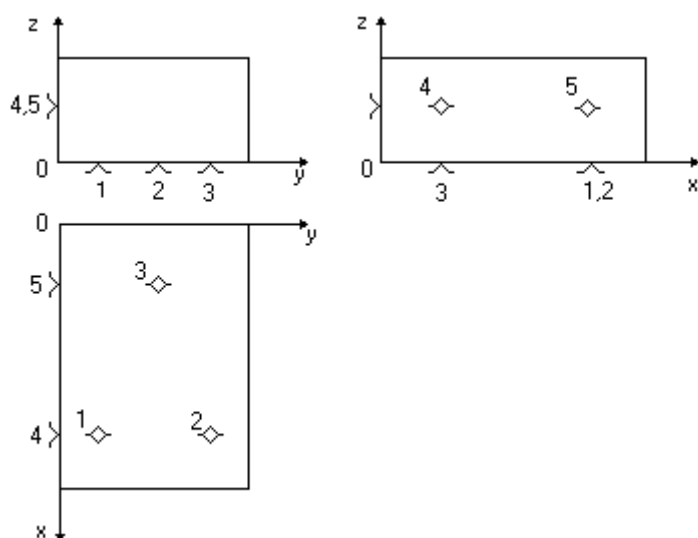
Пример расположения опорных точек на призматической заготовке
